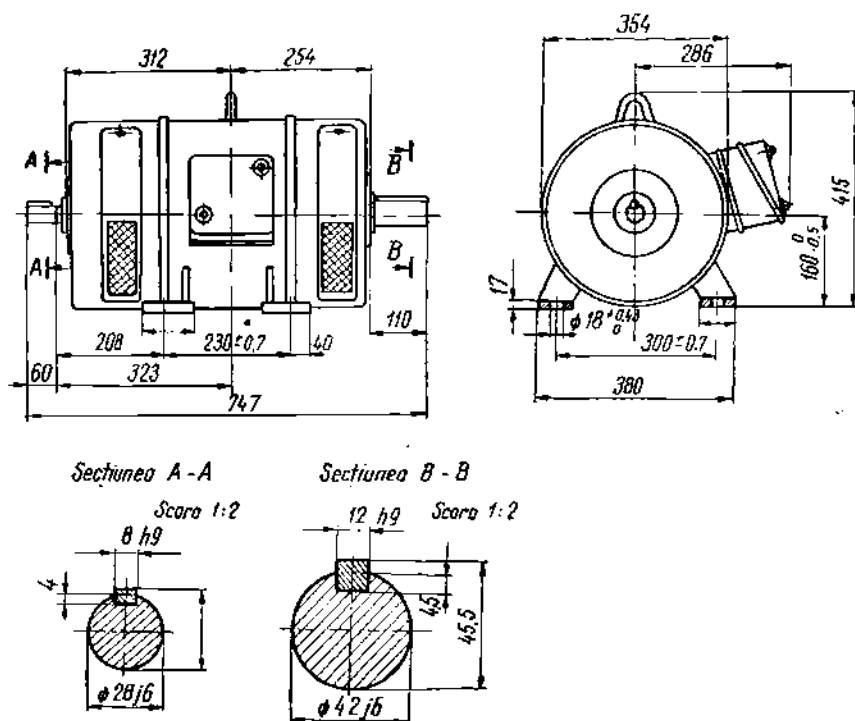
Motor tip Ce 160 MF—7 kW. Dimensiuni de montaj.
